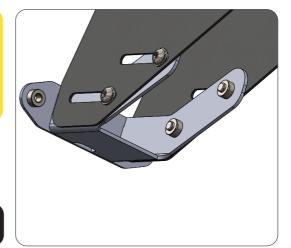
Detailansicht Querstreben Halter/detailed view cross strut bracket
